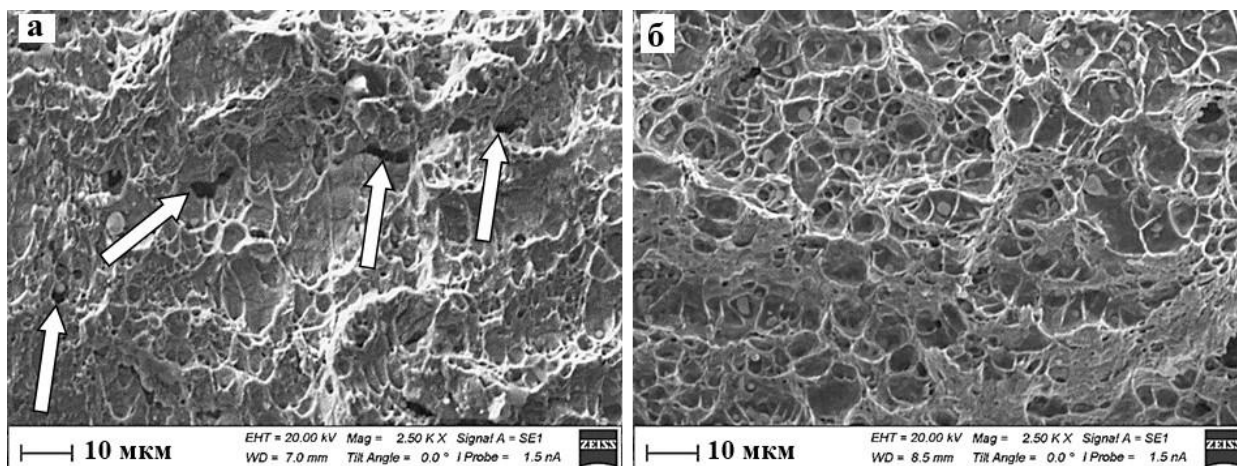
Поверхность вязкого излома металла сварного шва №1 (а) и №2 (б) (стрелками указаны микропоры)
